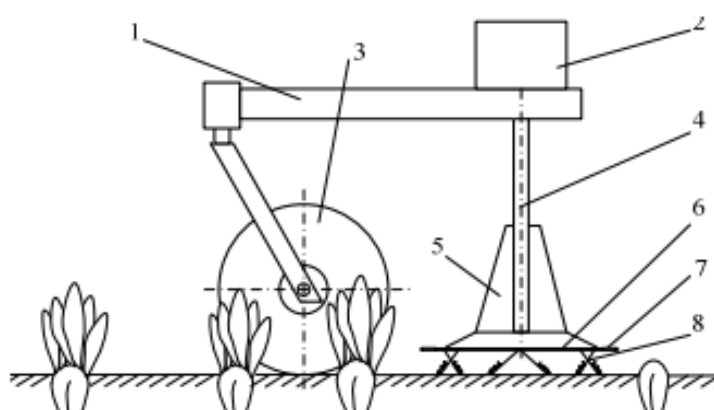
Апарат для зрізування гички та очищення головок коренеплодів: 1 – рама; 2 – редуктор; 3 – опорне колесо; 4 – вал; 5 – бітер; 6 – диск; 7 – ніж; 8 – очисний елемент.
